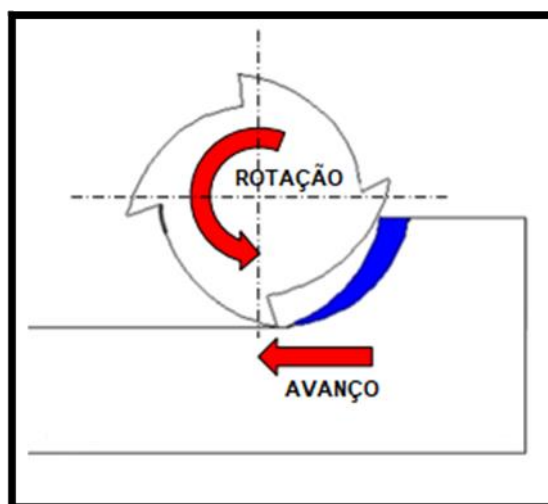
Representação esquemática de vista superior do método de fresamento discordante(10)
